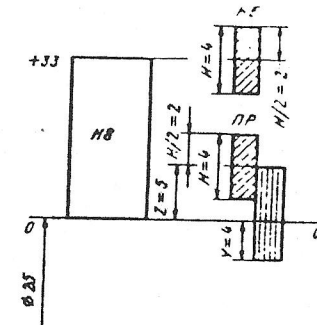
Схема расположения полей допусков калибра для размера 25H8
